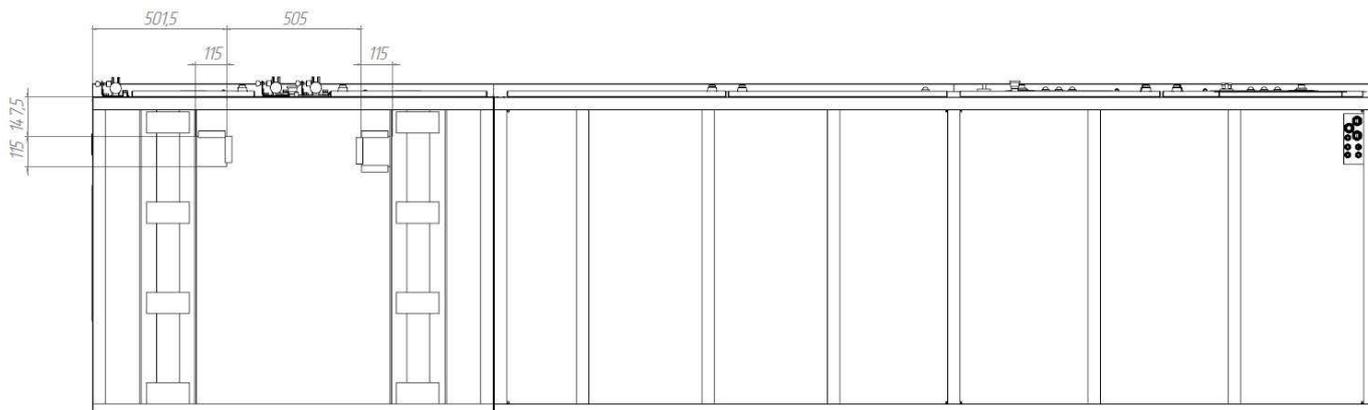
АТ27-М40...М63-6/6-XXXXXX-С-43. Вид снизу
